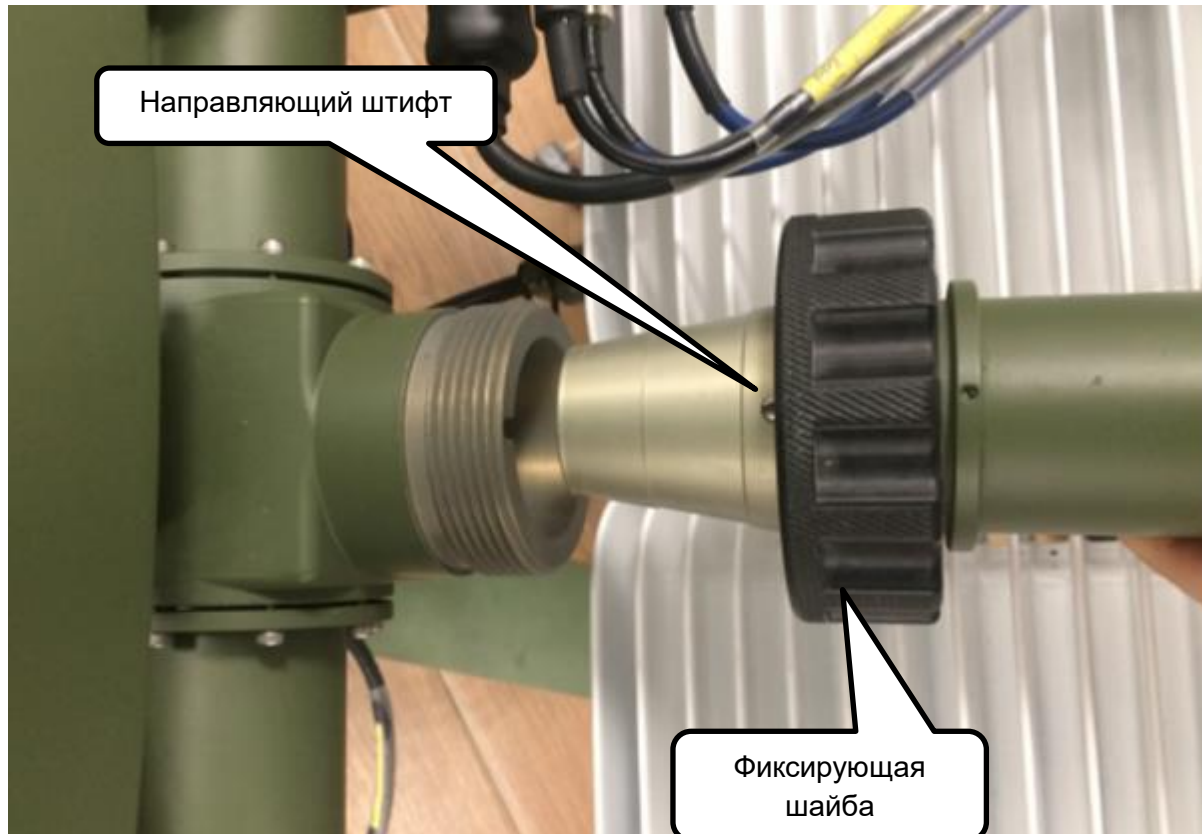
Сборка держателя облучателя
